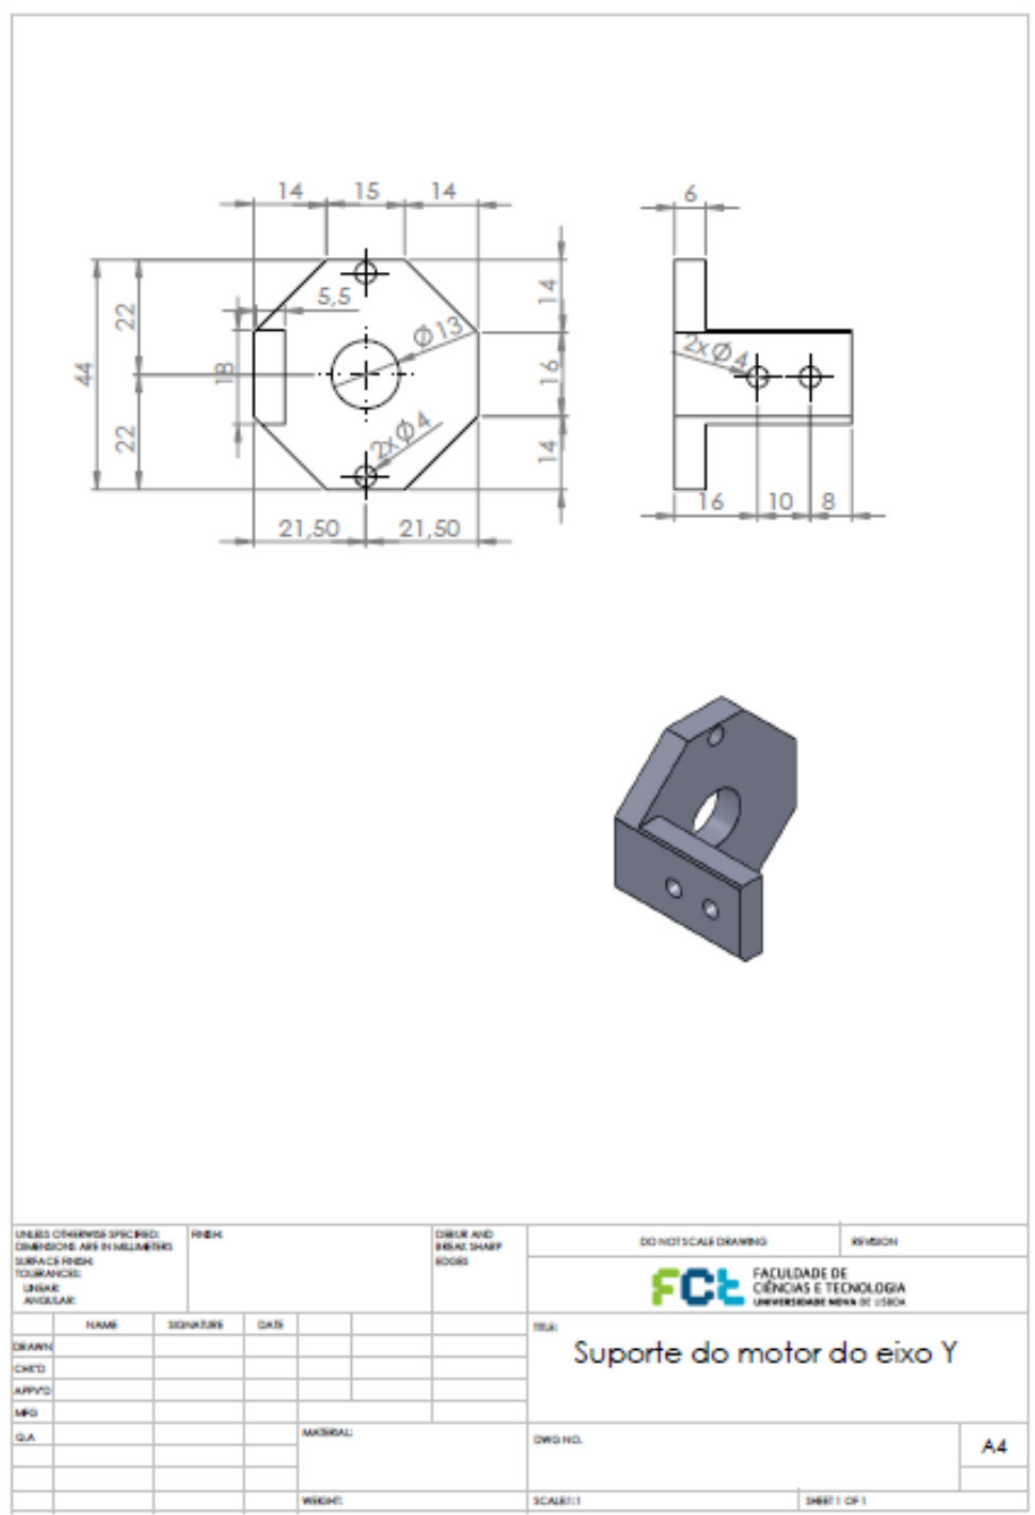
desenho técnico do suporte do motor do eixo Y.
